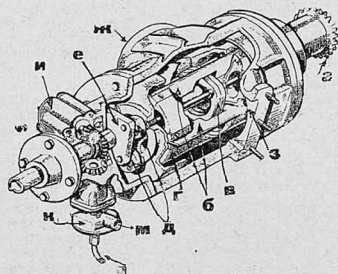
Схема устройства компрессора Джермерсон — Джиллетт.
